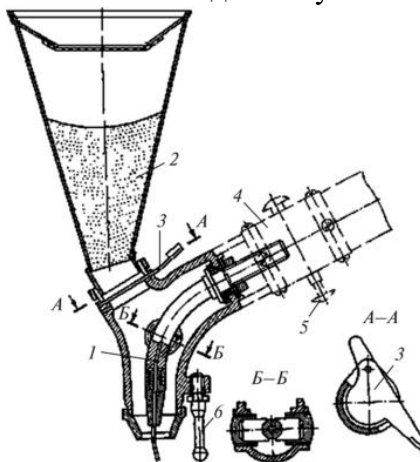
Полуавтоматическая сварка и наплавка под слоем флюса
